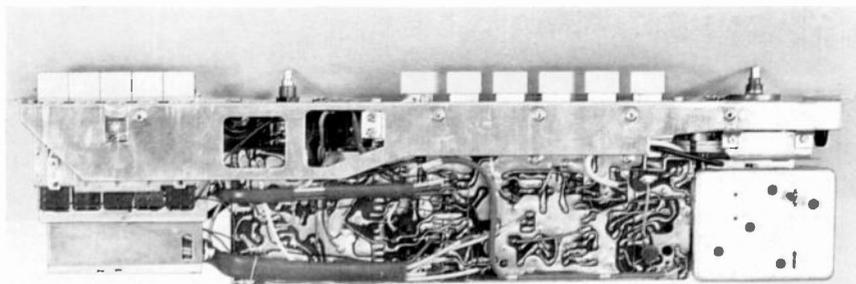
Untersicht des HF-1-Chassis mit Blick auf die Druckschaltungsplatte
